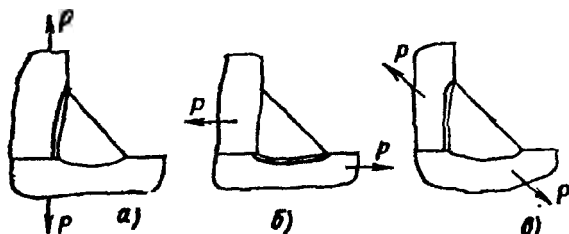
Схемы разрушения угловых швов, металл которых прочнее основного металла
